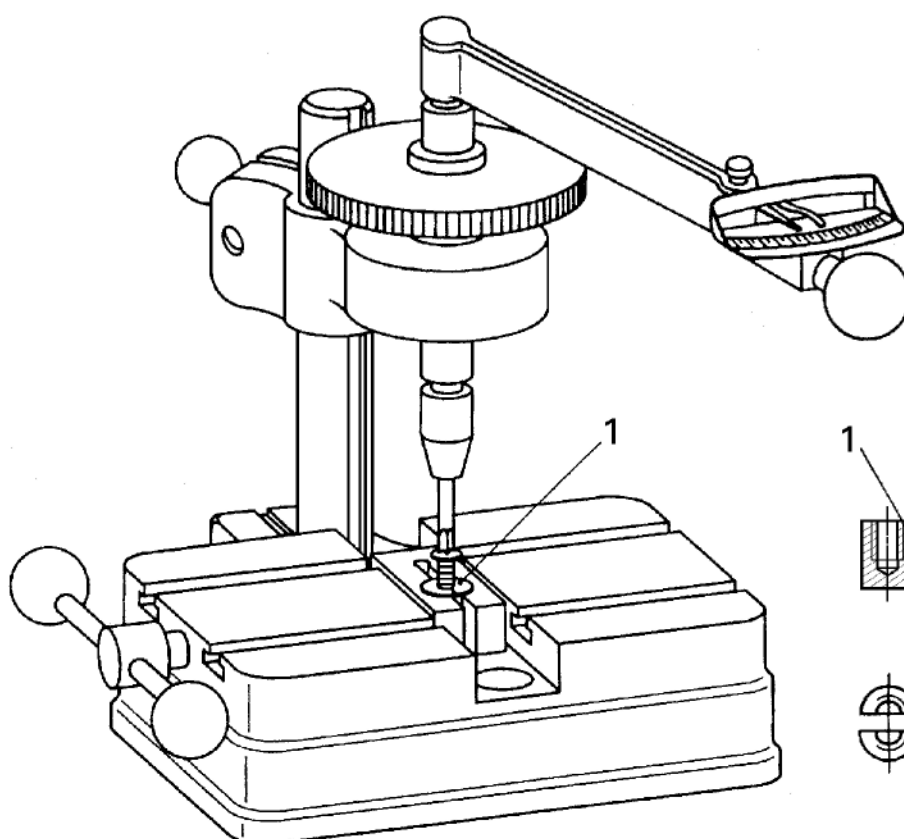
Испытательное устройство для испытаний на скручивание головки.
